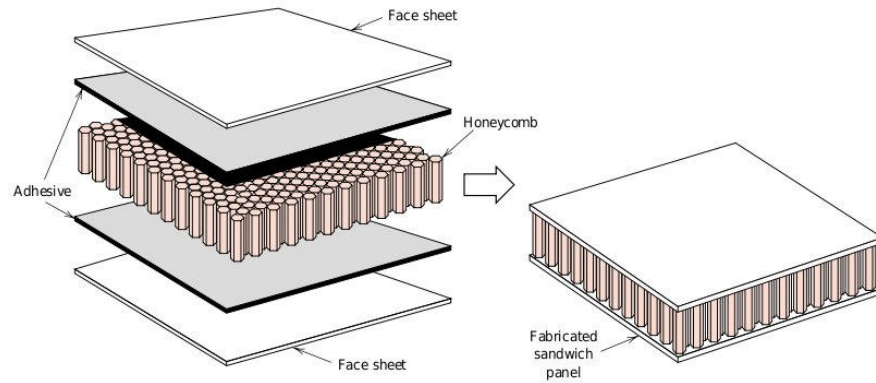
Estructura sándwich con núcleo nido de abeja.
